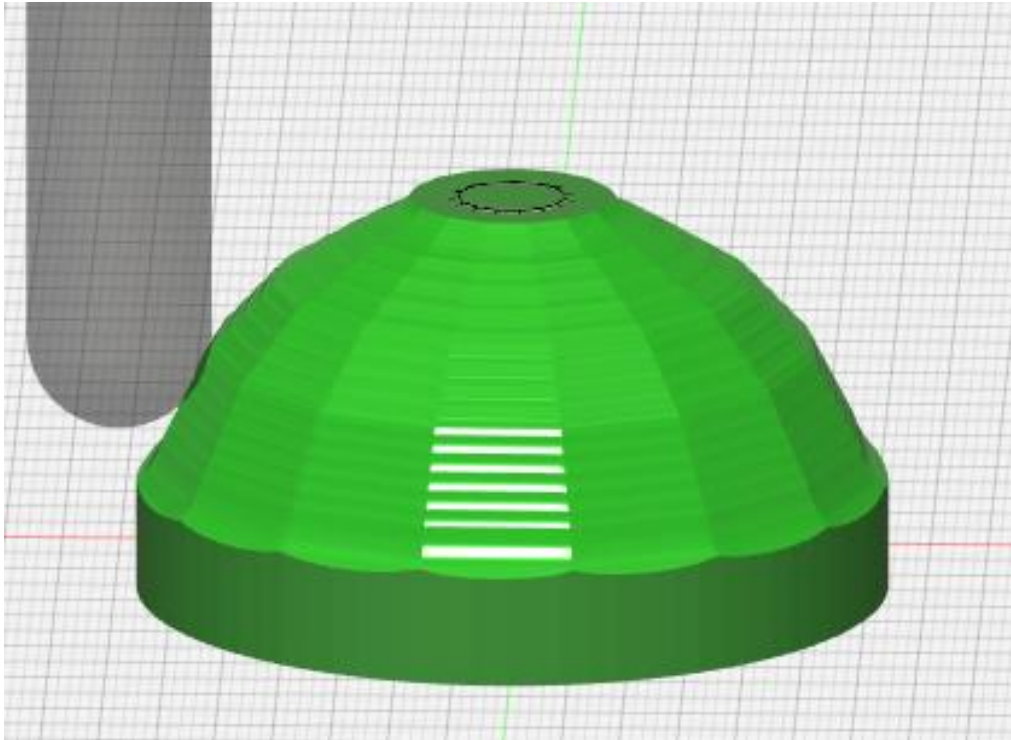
Zobrazení diskokoule po hrubování na 3 osém CNC centru [38]
